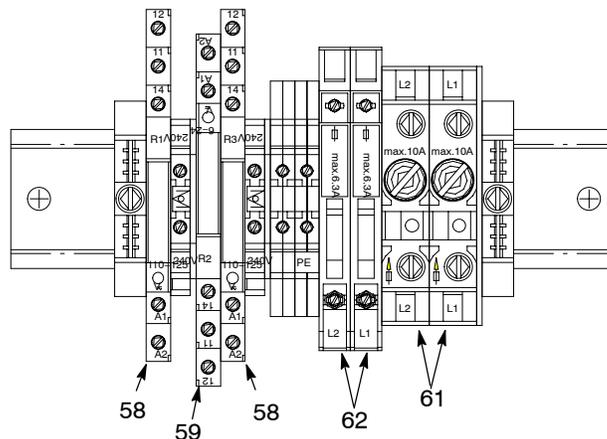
Реле и предохранители управления нового типа – детали консоли (5 из 5)
